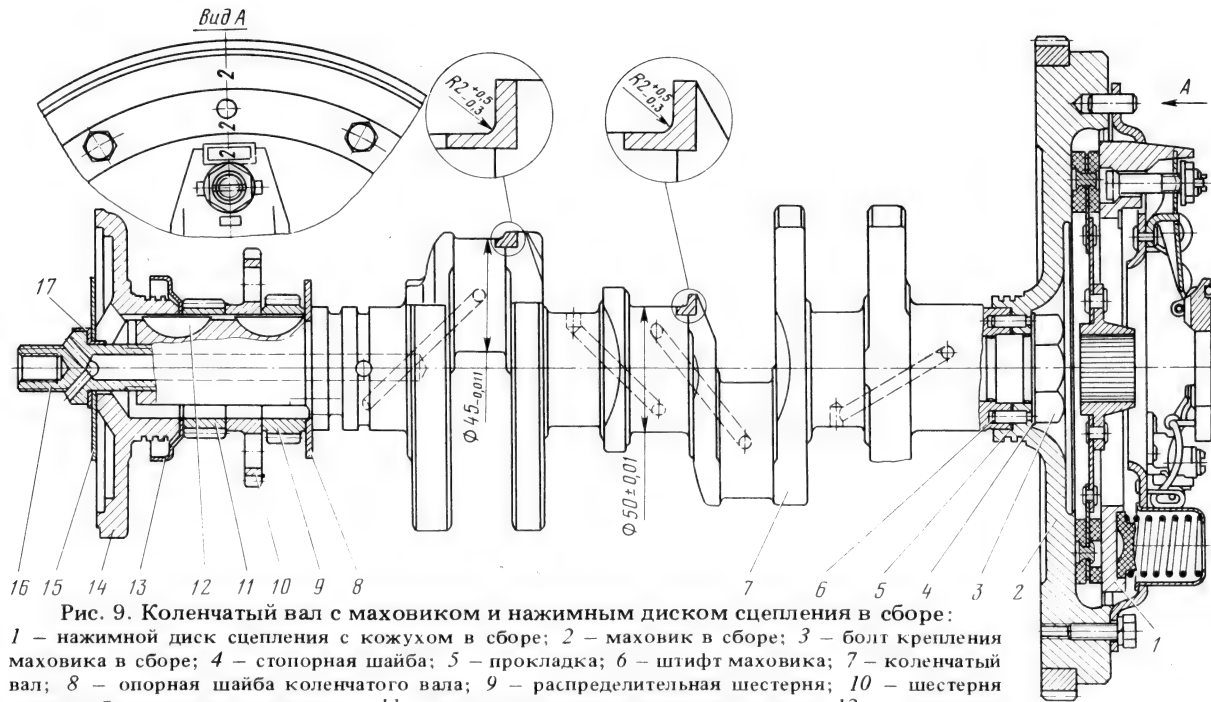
Коленчатый вал с маховиком и нажимным диском сцепления в сборе:
